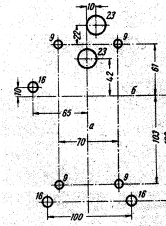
Сверление отверстий для установки на изоляционных плитах контакторов типа КП 503 и КП 513 с задним присоединением
